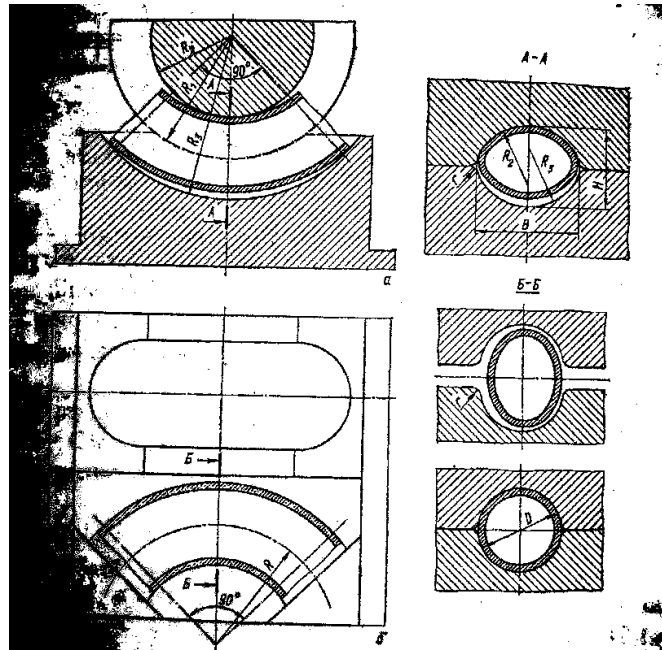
Схема деформування труби-заготовки під час штампування крутозігнутих відводів
